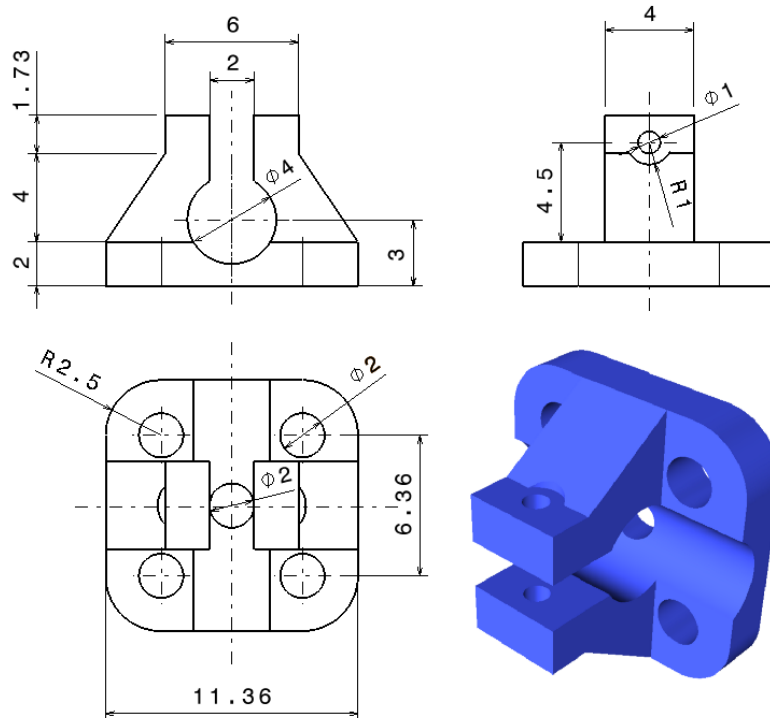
Vistas del anclaje del motor a la barra. Cotas en mm
